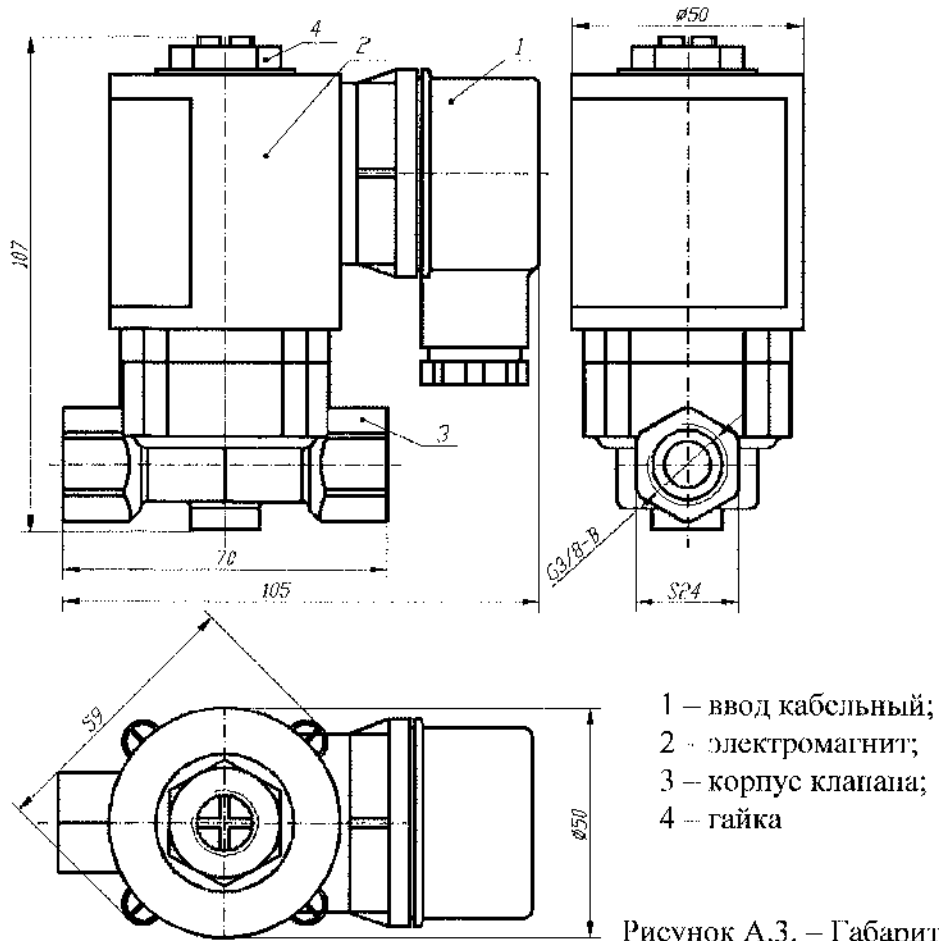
Габаритные и установочные размеры клапана КИ 93-10
